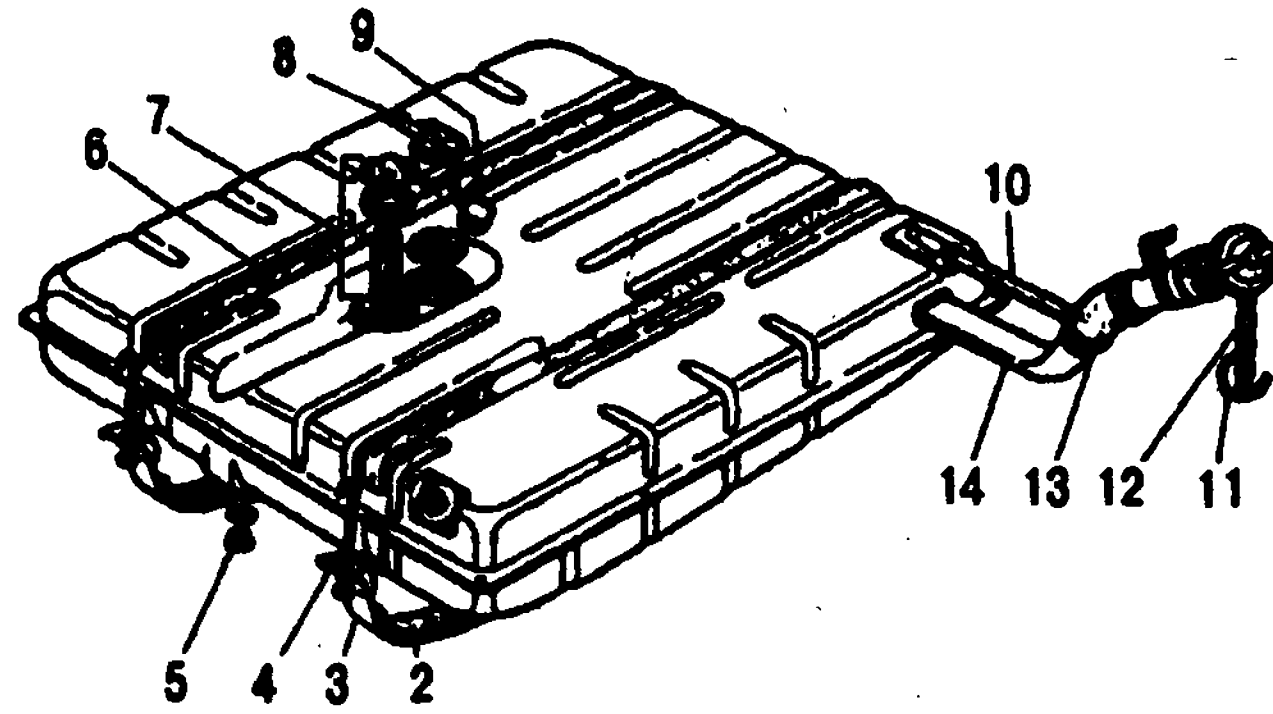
Топливный бак: 2 и 6 - прокладки; 3 - лента; 4 - крючок; 5 - пробка сливного отверстия; 7 - топливозаборник; 8 - датчик электрического указателя уровня топлива; 9 - поплавок; 10 - воздушный шланг; 11 - кольцо; 12 - цепочка; 13 - шланг; 14 - наливная горловина
